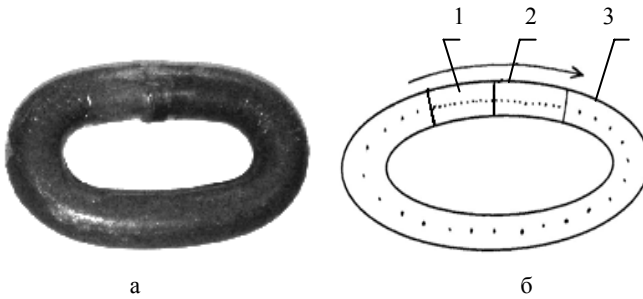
Загальний вид ланки після зварювання - а і схема виміру твердості по поверхні ланки - б: 1 – зона термічного впливу; 2 – місце зварювання; 3 – основний метал
